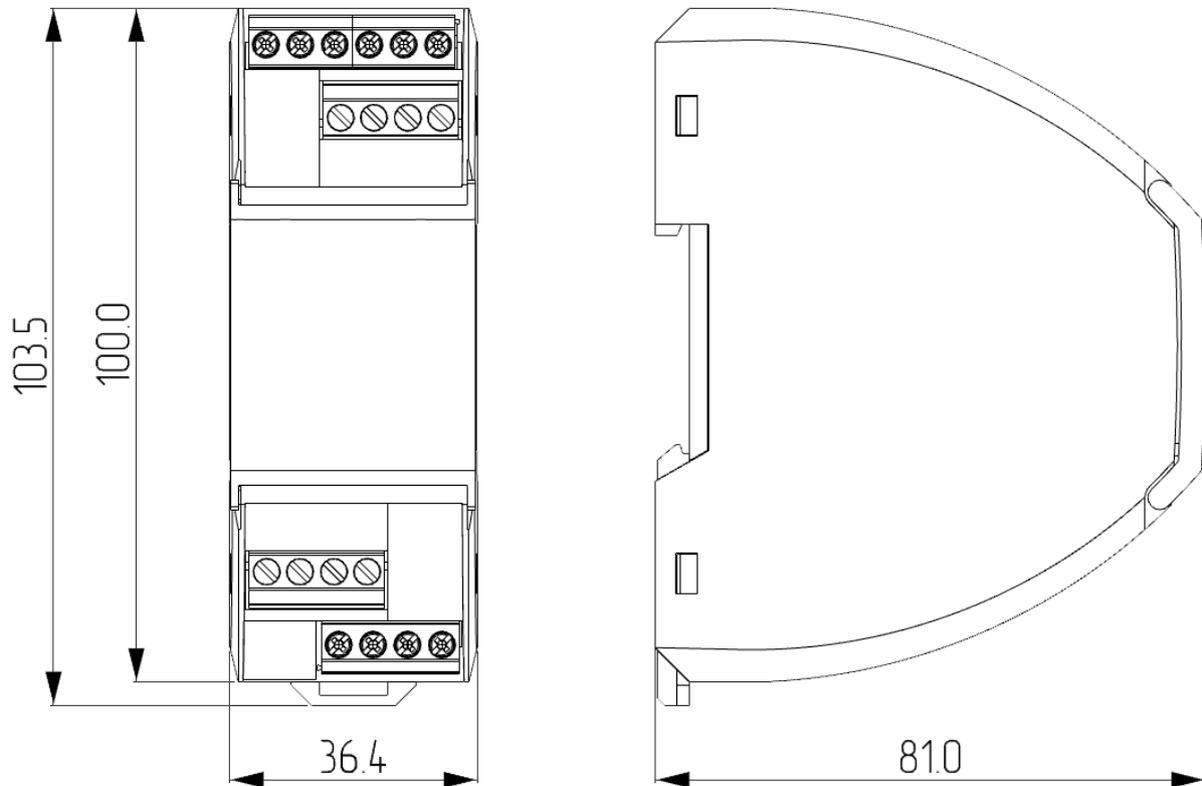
Габаритный чертеж ИСИ1625
